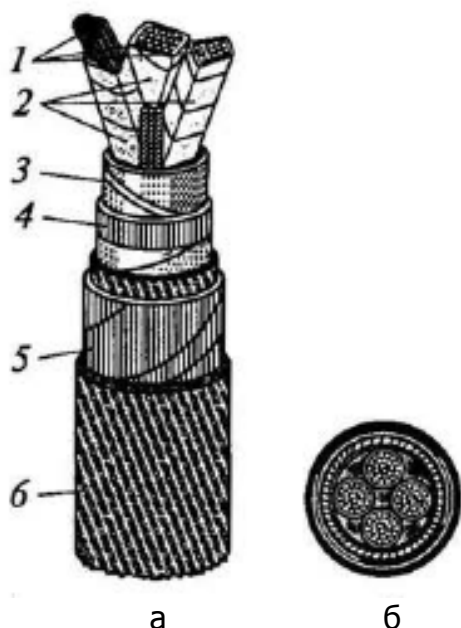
Кабель силовой с бумажной пропитанной изоляцией, бронированный:
